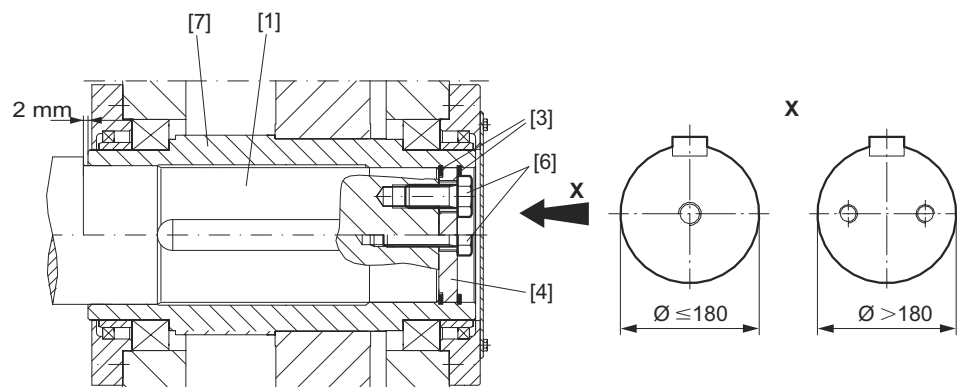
Montage Horizontalgetriebe mit Passfederverbindung
